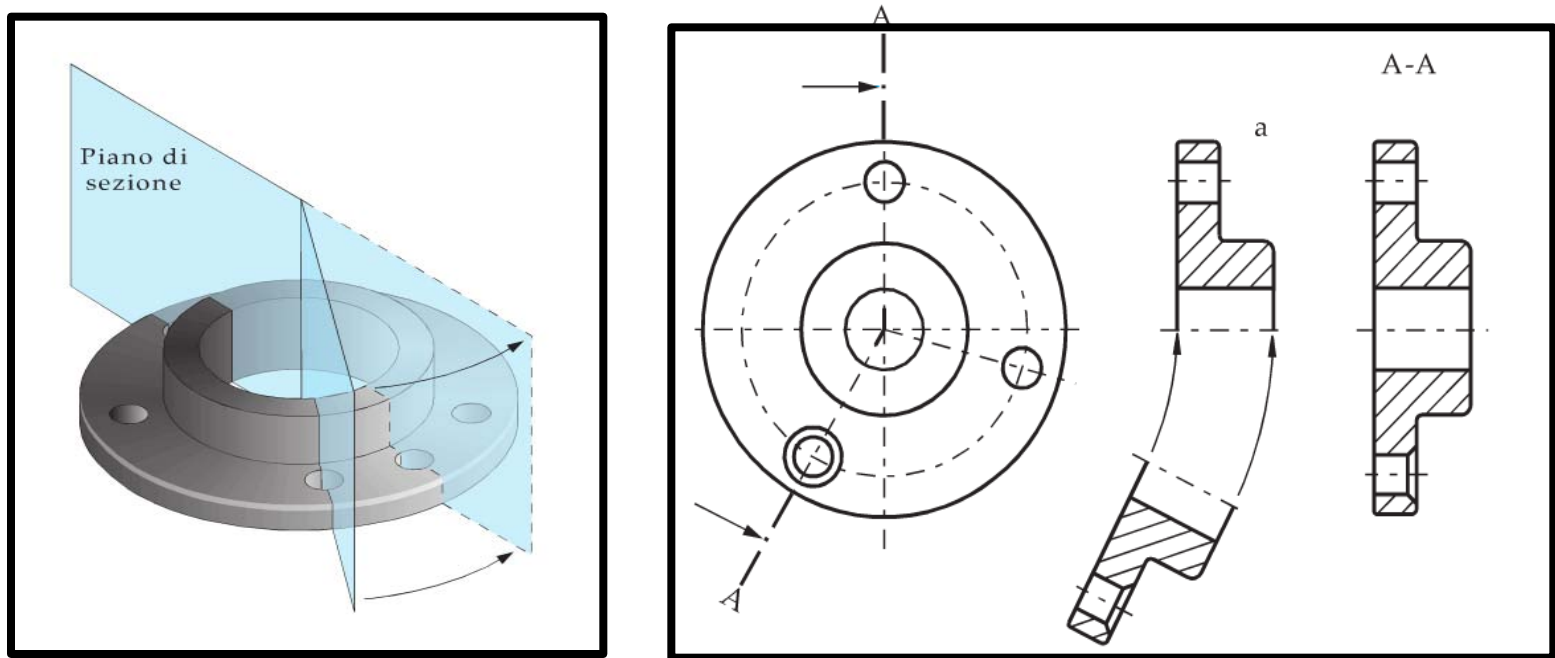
Sezione con due piani consecutivi in cui la sezione (a) rappresenta il passaggio intermedio
